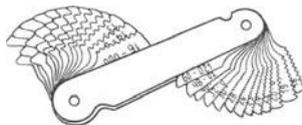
Gewindeschablonen für Innen- und Außengewinde.
